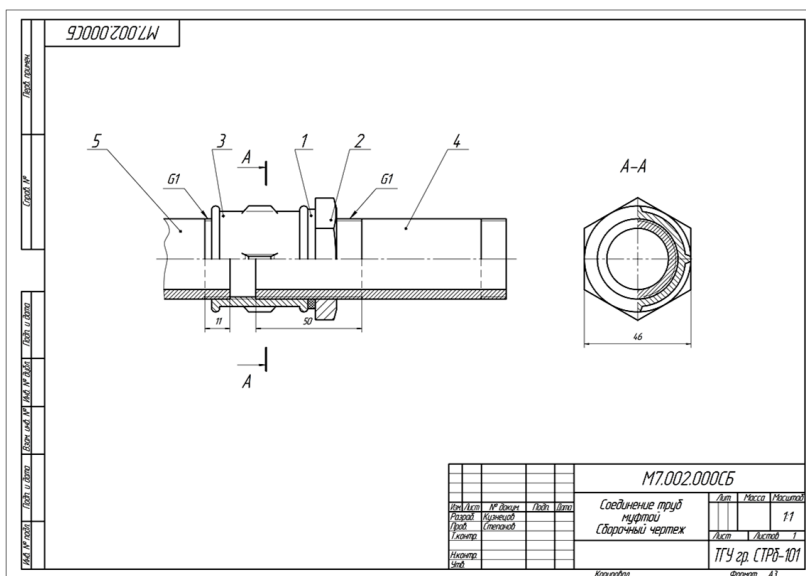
Пример выполнения сборочного чертежа трубного соединения
